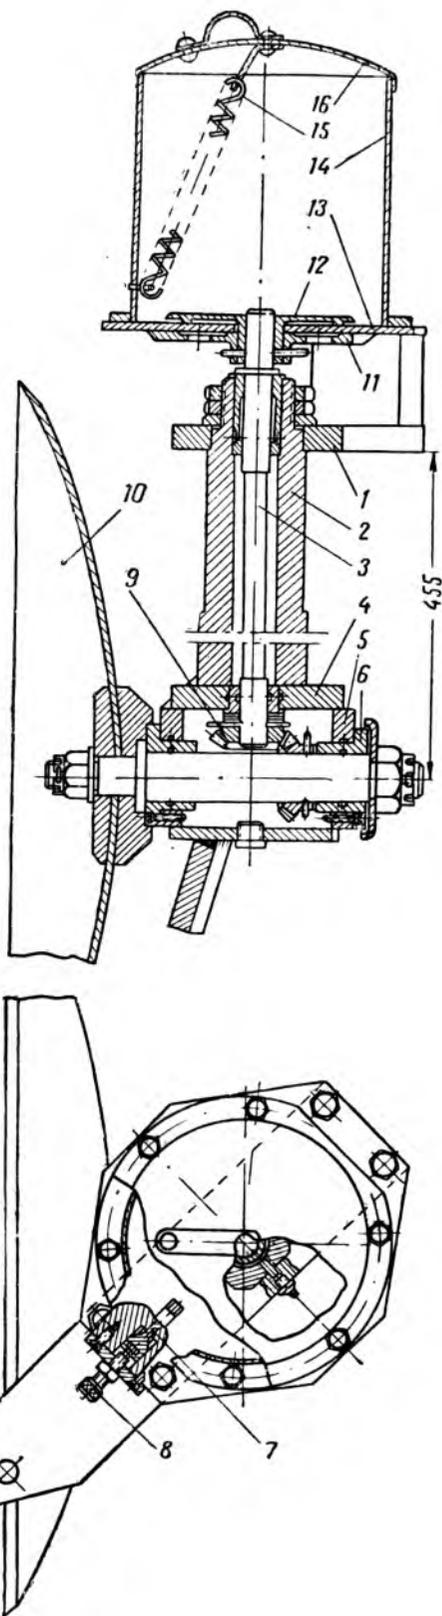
Рабочий орган: 1 — кронштейн; 2 — труба стойки; 3 — вал высевяющего аппарата; 4 — коробка редуктора; 5 — втулка; 6 — вал сферического диска; 7 — ползун; 8 — винт; 9 — шестерня коническая; 10 — диск сферический; 11 — диск нижний; 12 — диск верхний; 13 — плита; 14 — семенной бункер; 15 — пружина; 16 — крышка бункера.
